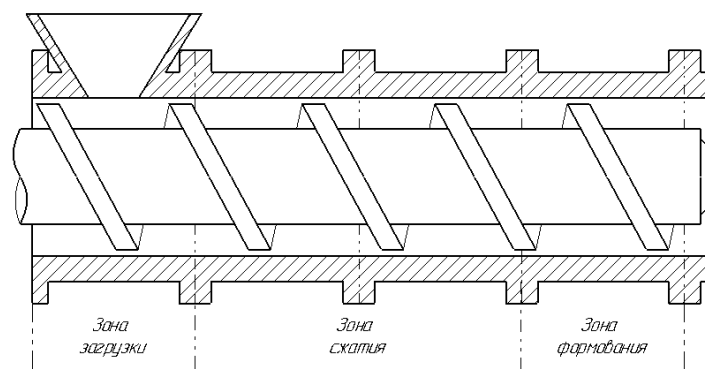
Конструкция шнекового пресса фрезформовочной машины
